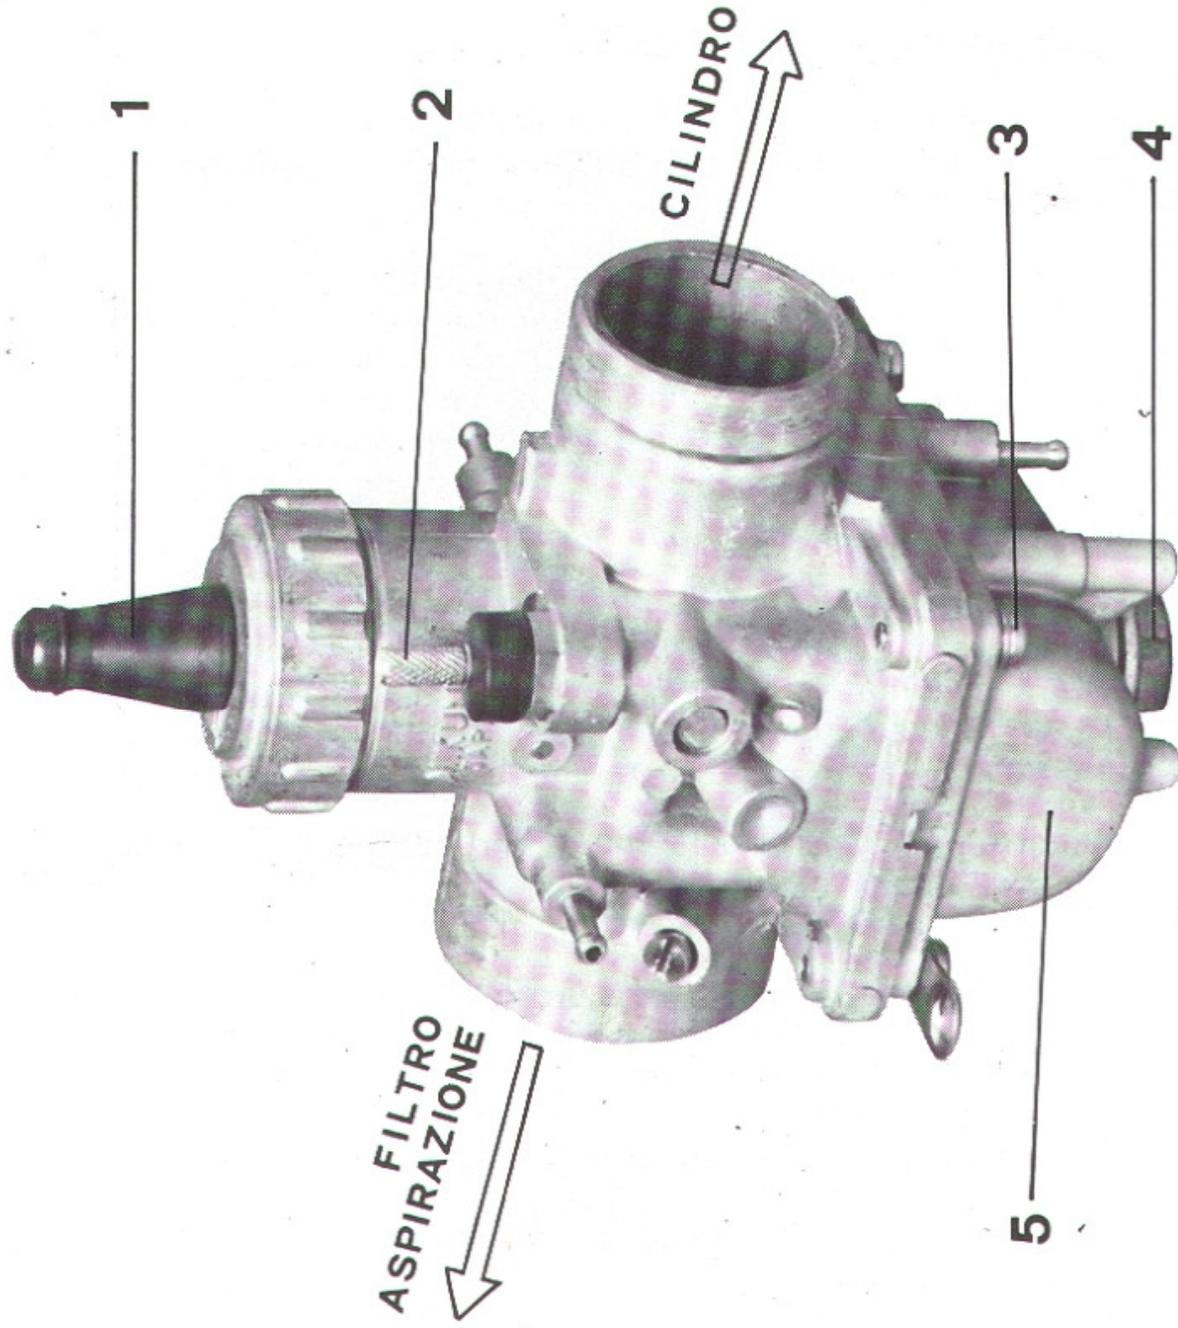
CARBURATORE MIKUNI SE VM 26
